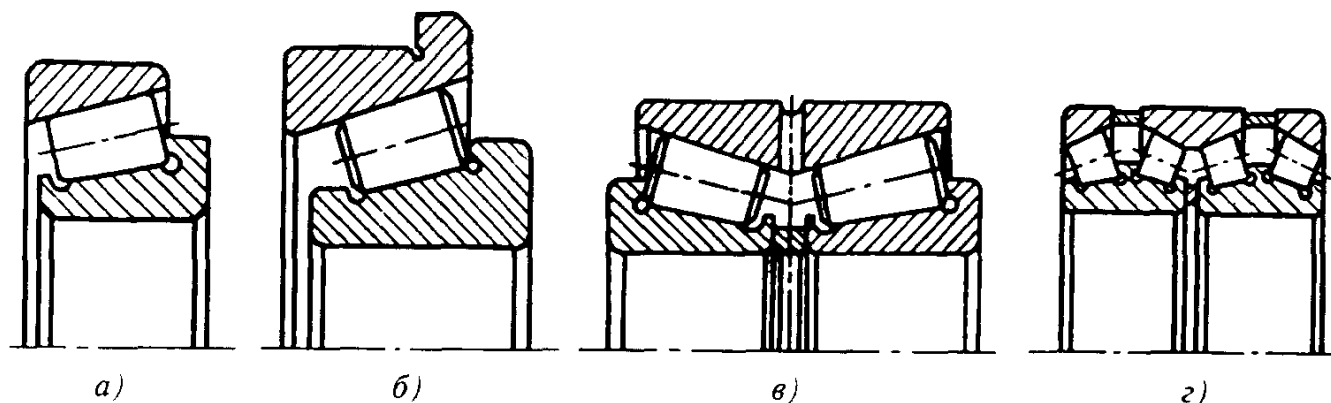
Подшипники радиально-упорные роликовые исполнений:
